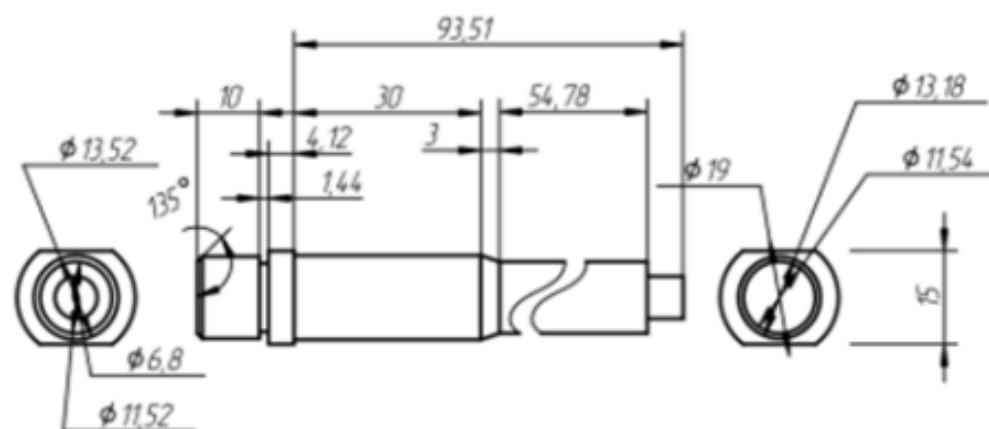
Приспособ. для крепления колеса. Обозначения соответствуют чертежам.
